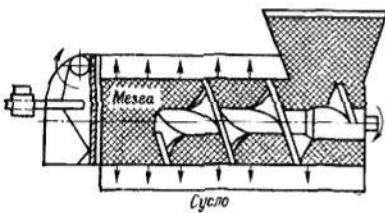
Схема шнекового пресса, обеспечивающего перемещение мезги по дренирующей поверхности с одновременным сжатием
